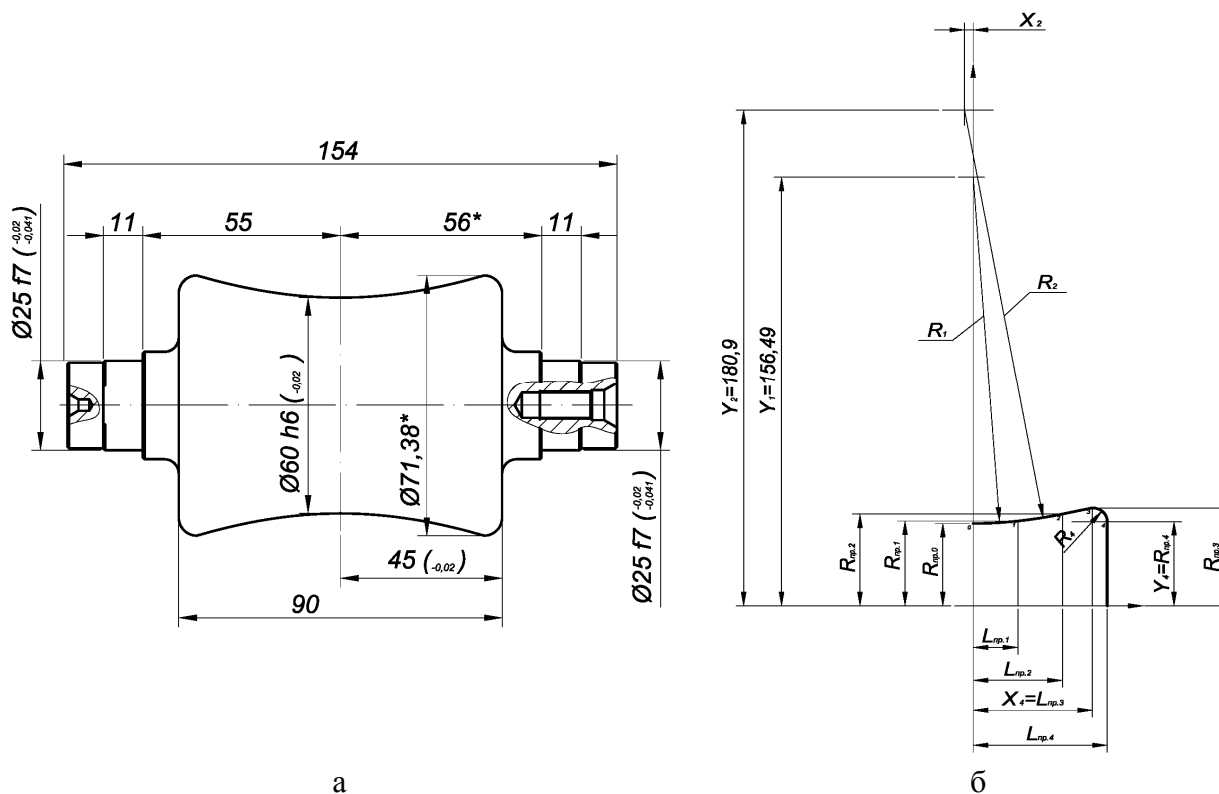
Калибровка рабочих валков. Общий вид валка (а), профиль бочки валка (б)
